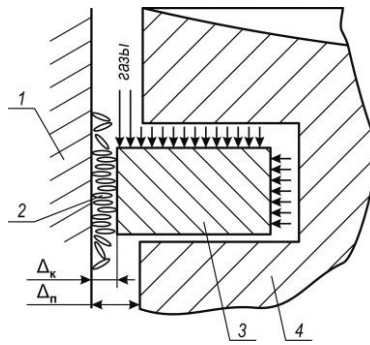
Модель трибологической системы цилиндрическая втулка – смазочный материал – поршневое кольцо/поршень: 1 – втулка цилиндра; 2 – смазочный материал; 3 – кольцо; 4 – поршень
